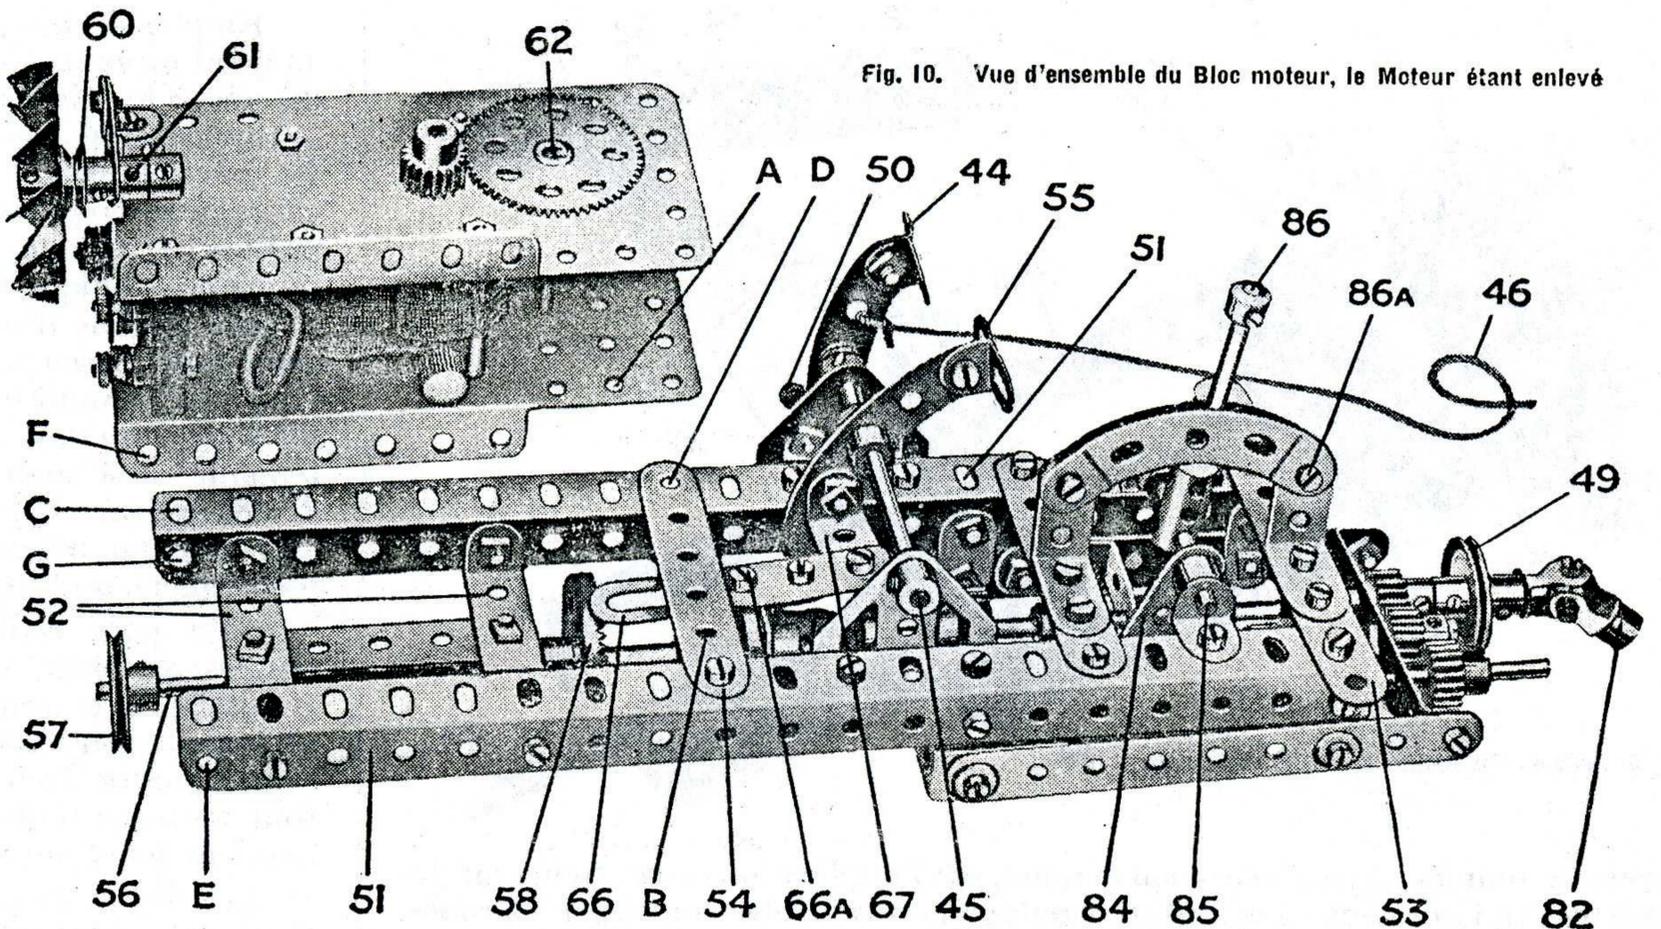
Vue d'ensemble du Bloc moteur, le Moteur étant enlevé
